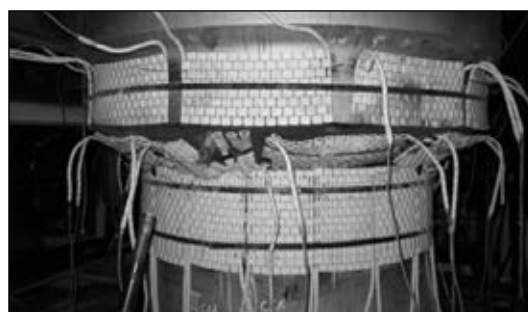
Расположение нагревателей на приспособлении для нагрева внутренней стороны сварного соединения
